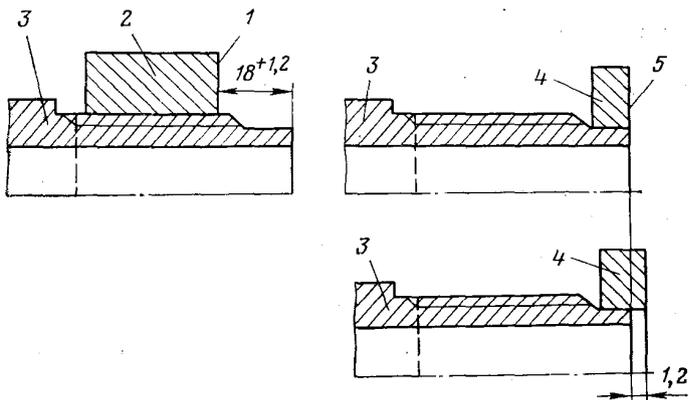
Контроль калибрами трубы резьбового соединения насосно-компрессорных труб НКБ:
